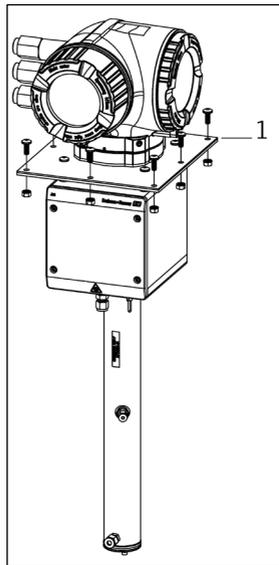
Halterung für Montage auf einem Befestigungsblech und Befestigungsmaterialien für J22
